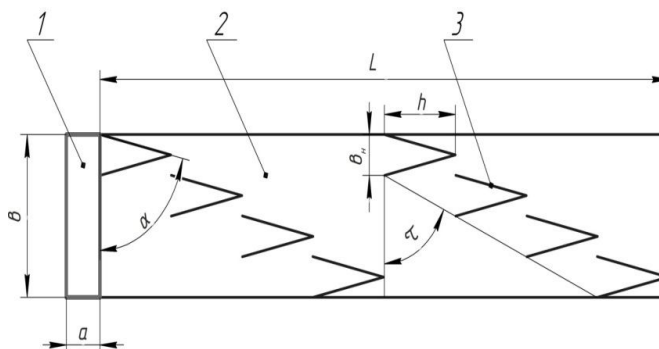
Схема развертки поверхности режущего барабана скользящего резания: 1 – горловина, 2 – поверхность барабана, 3 – V-образный нож
